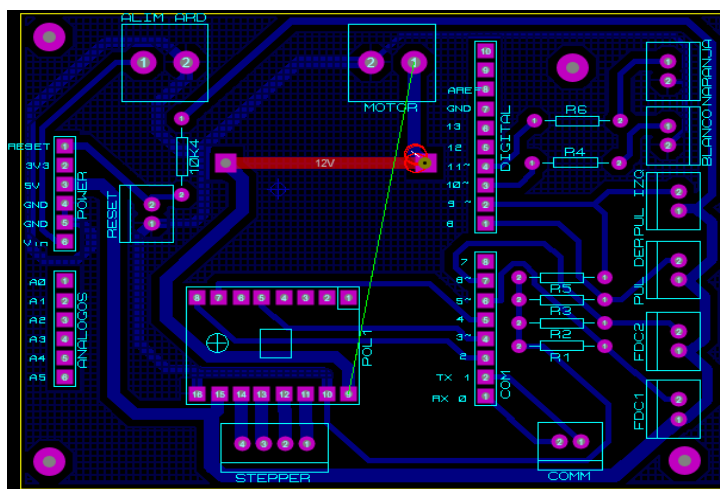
Diseño de la placa PCB de la Bomba de Jeringa
